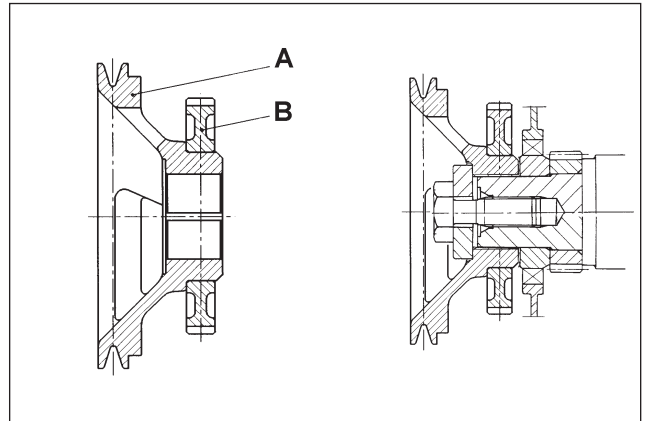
Dans le cas de moteur doté de régulateur électronique, monter sur la poulie de vilebrequin A la roue phonique B. Avant le montage de la roue, enduire de Loctite 648 les surfaces de contact des deux pièces. Monter la poulie sur le vilebrequin et la fixer au moyen de la vis munie de sa rondelle d'appui, en lubrifiant d'abord le filetage à l'huile moteur. Ensuite, serrer la vis au couple de 60+70 Nm (6+7 kgm) puis au couple de 340 Nm (34 kgm).
